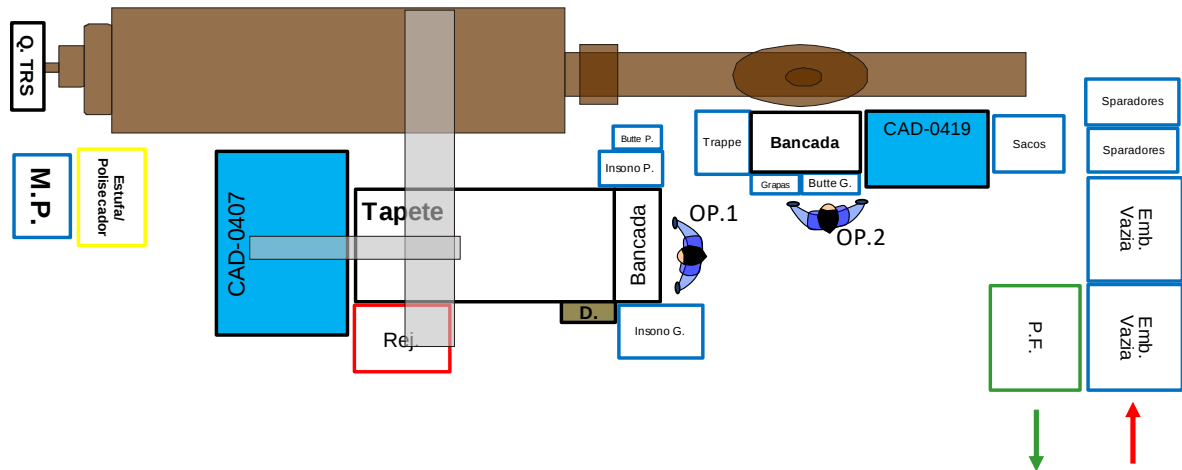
Layout do posto de injeção do molde 9298 com redução de MOD
